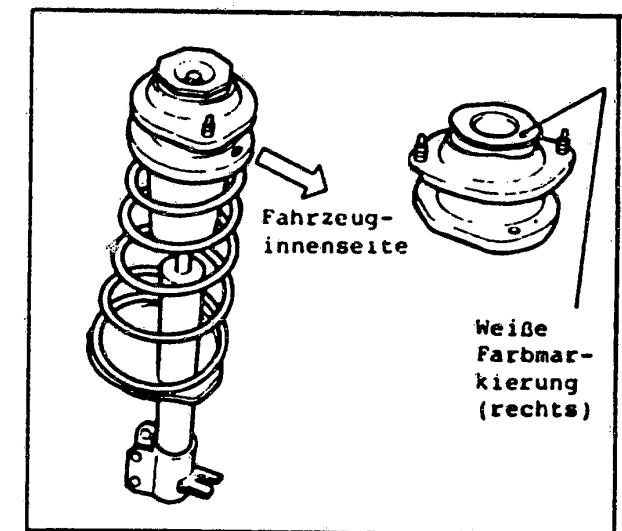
Ausrichtung des hinteren Federbeins zum Einbau.
